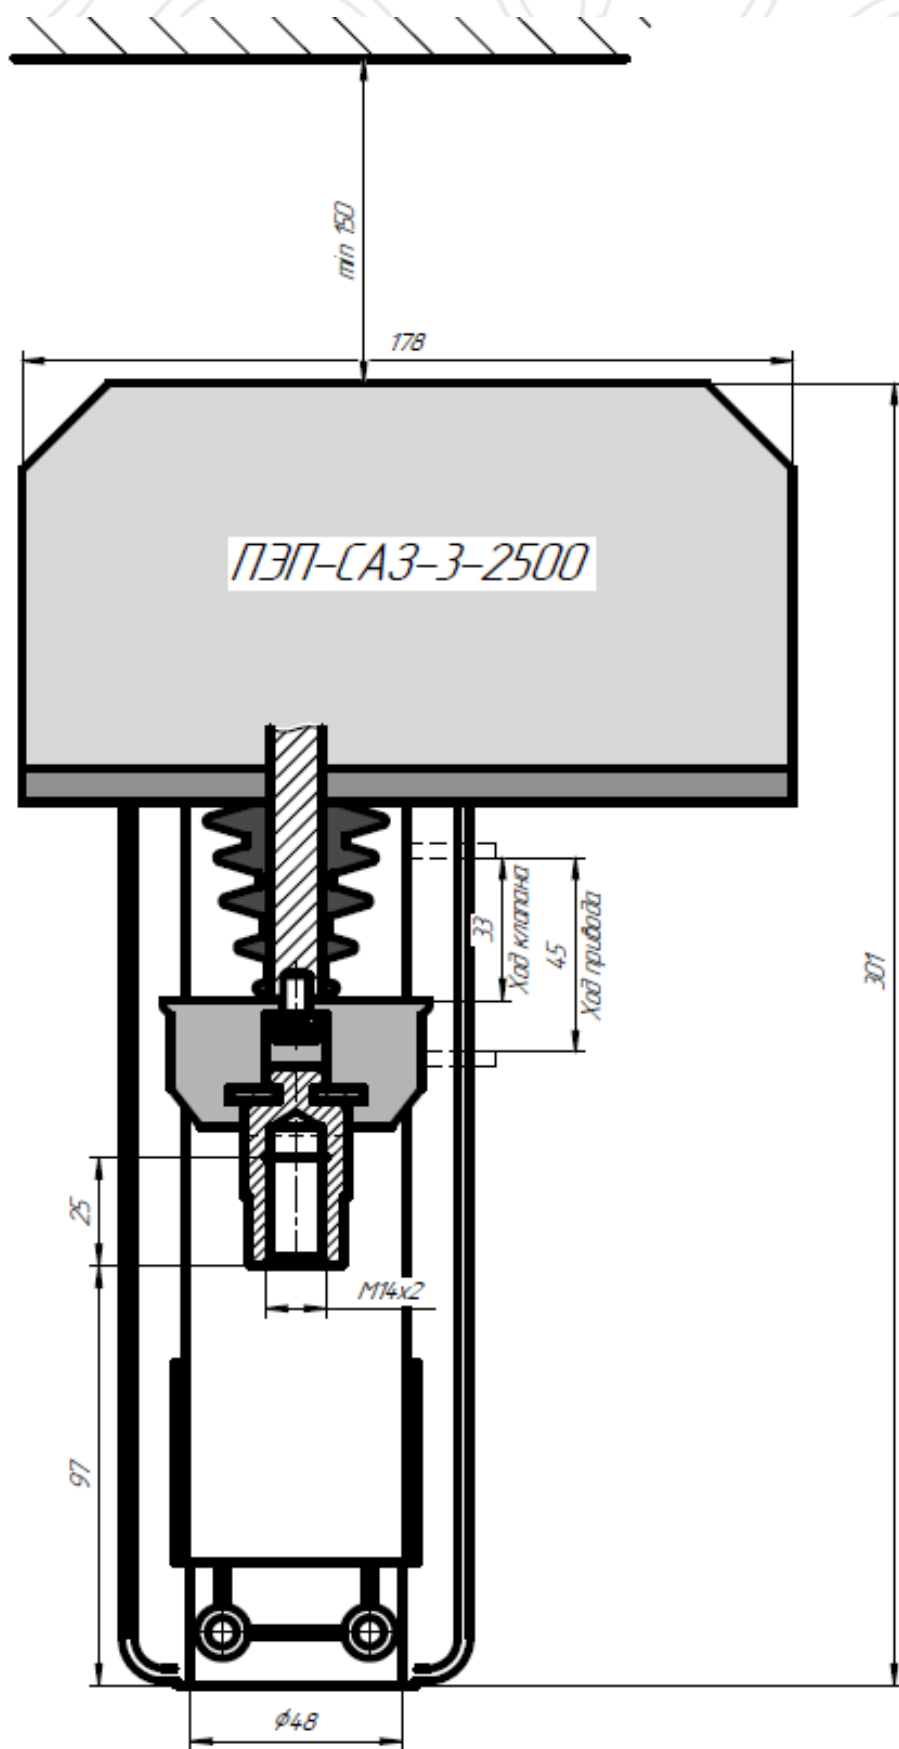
Габаритные и присоединительные размеры ПЭП-СА3-3-2500
